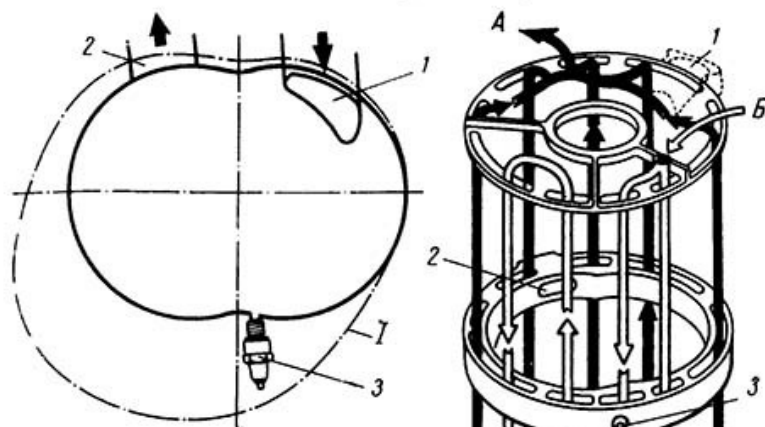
Схема циркуляции охлаждающей жидкости в корпусах РПД RC1-60 и температурное поле корпуса:
